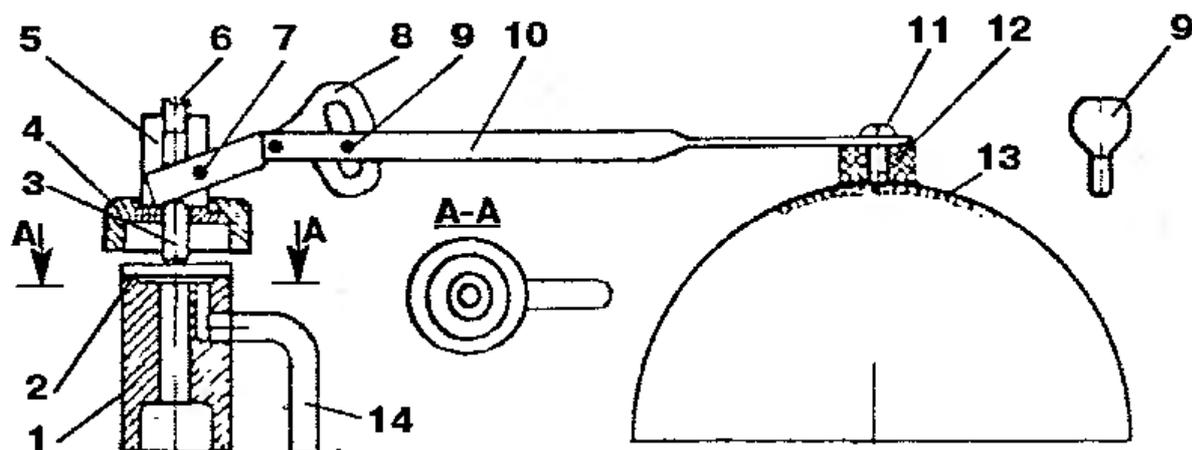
Вертикальный поплавковый клапан: 1 — корпус клапана; 2 — резиновая прокладка; 3 — шток; 4 — накидная гайка; 5 — валик; 6 — специальный винт; 7 — шплинты; 8 — рычаг фасонный; 9 — барашек; 10 — рычаг поплавка; 11 — винт; 12 — втулка пластмассовая; 13 — поплавок; 14 — трубка сливная
